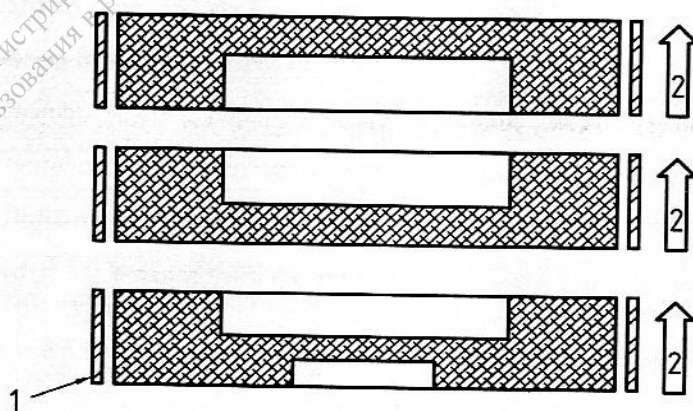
Типичный сменный элемент графитовой разрывной мембраны с держателем
